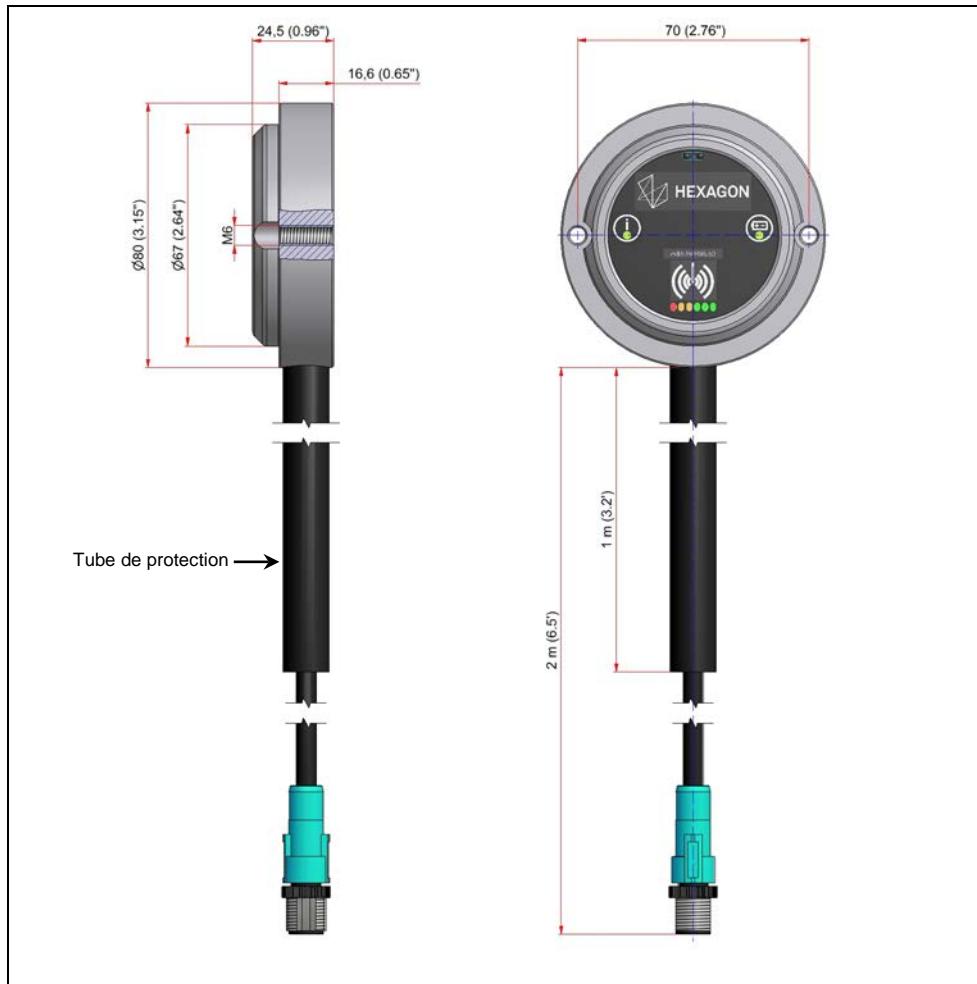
Dimensions RWR95.50-R-PLUG-8 (sortie radiale de câble)
